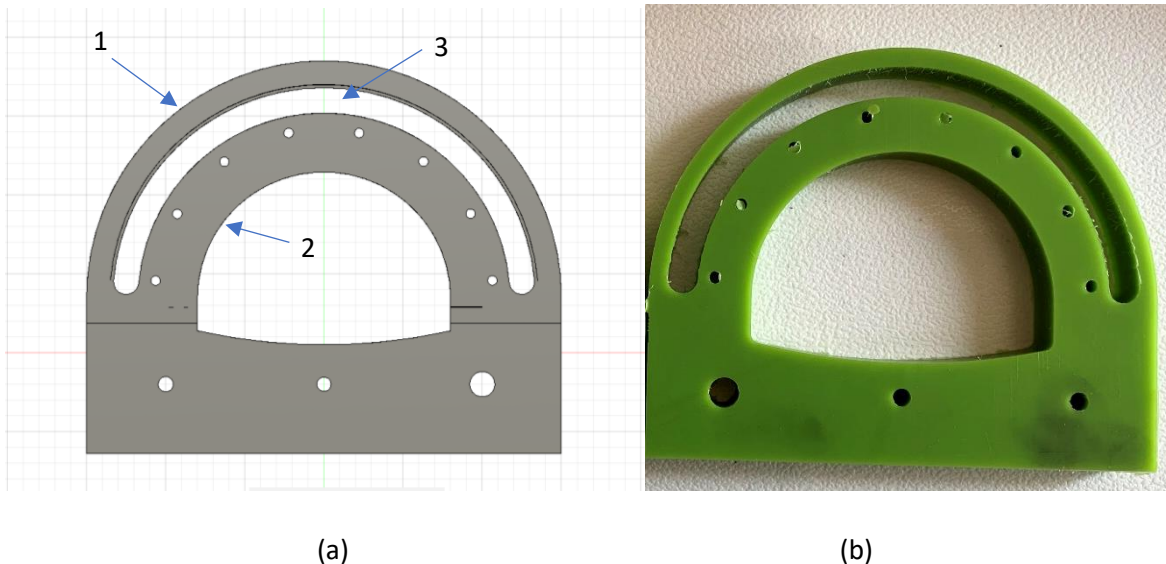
(a) Vista frontal de la pieza a manufacturar en Nylamid XL en fresadora. (b) Pieza manufacturada
